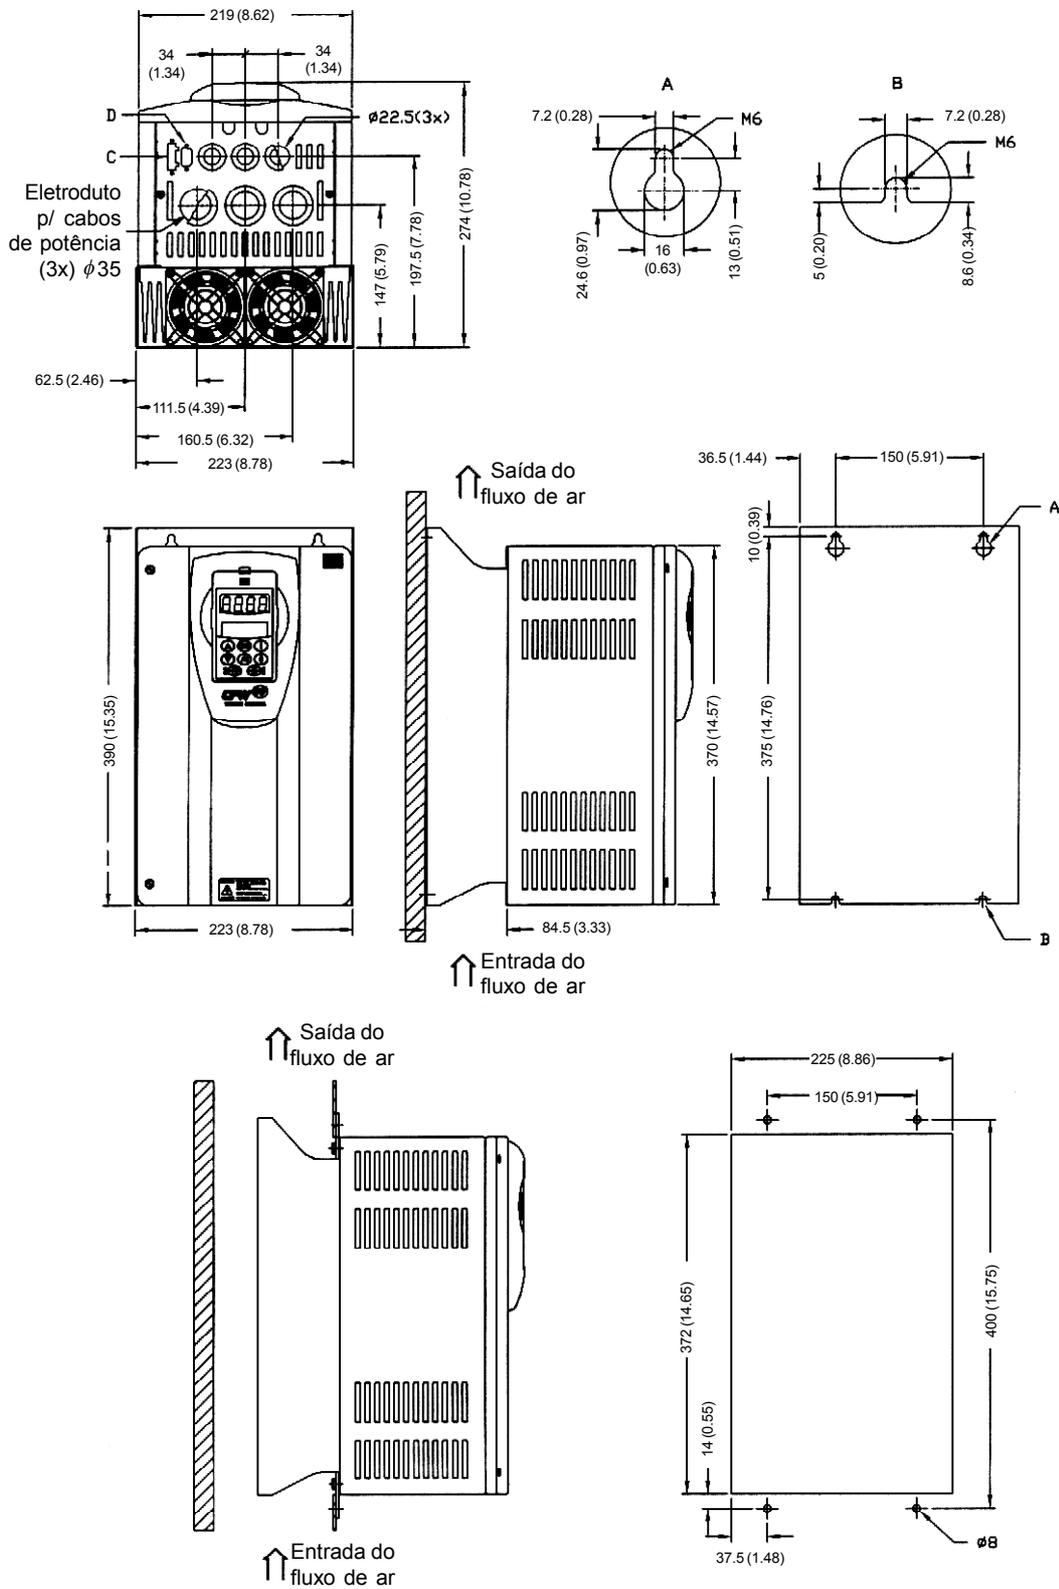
Mecânica 3 - Dimensões em mm (polegadas)
